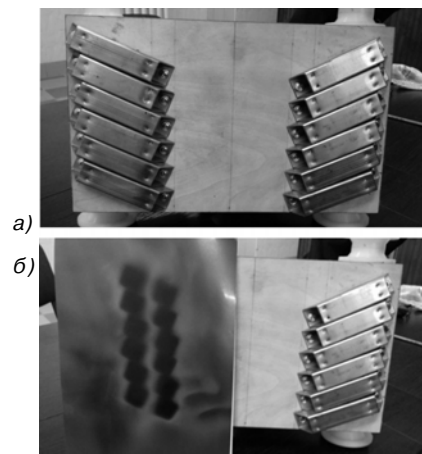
Общий вид магнитной сборки: а) – общий вид сборки магнитного полюса; б) – распределение магнитного поля сборки
